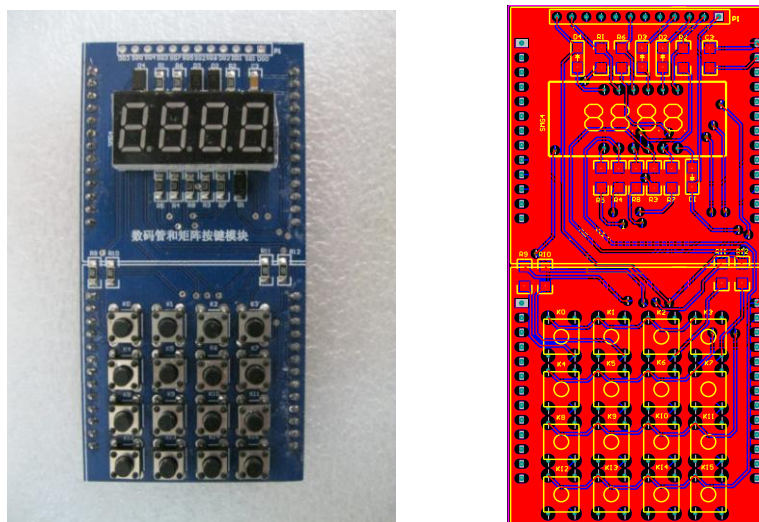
矩阵键盘及数码管模块实物图及 PCB 图
